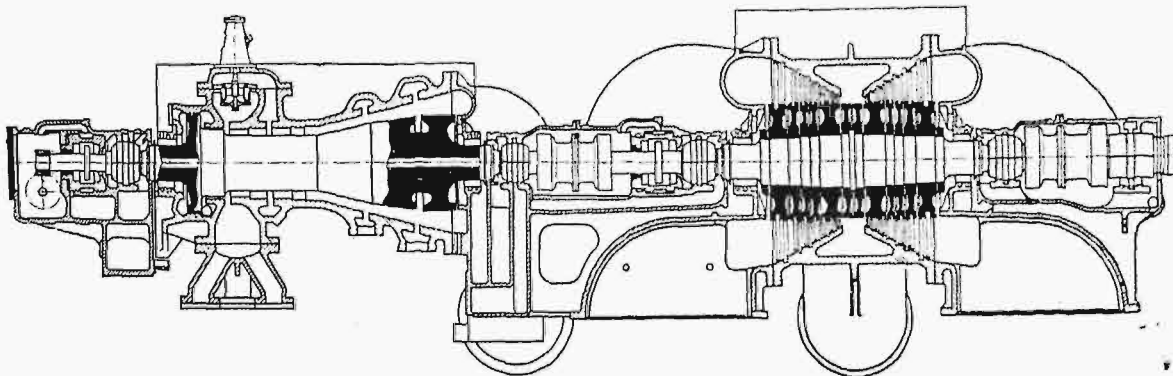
Reakcyjna turbina jednokadłubowa Parsons'a o mocy 12000 kW przy 3000 obr./min.
